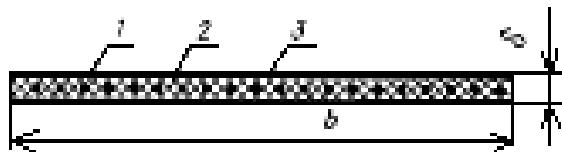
Кордошнуровый прорезиненный ремень
